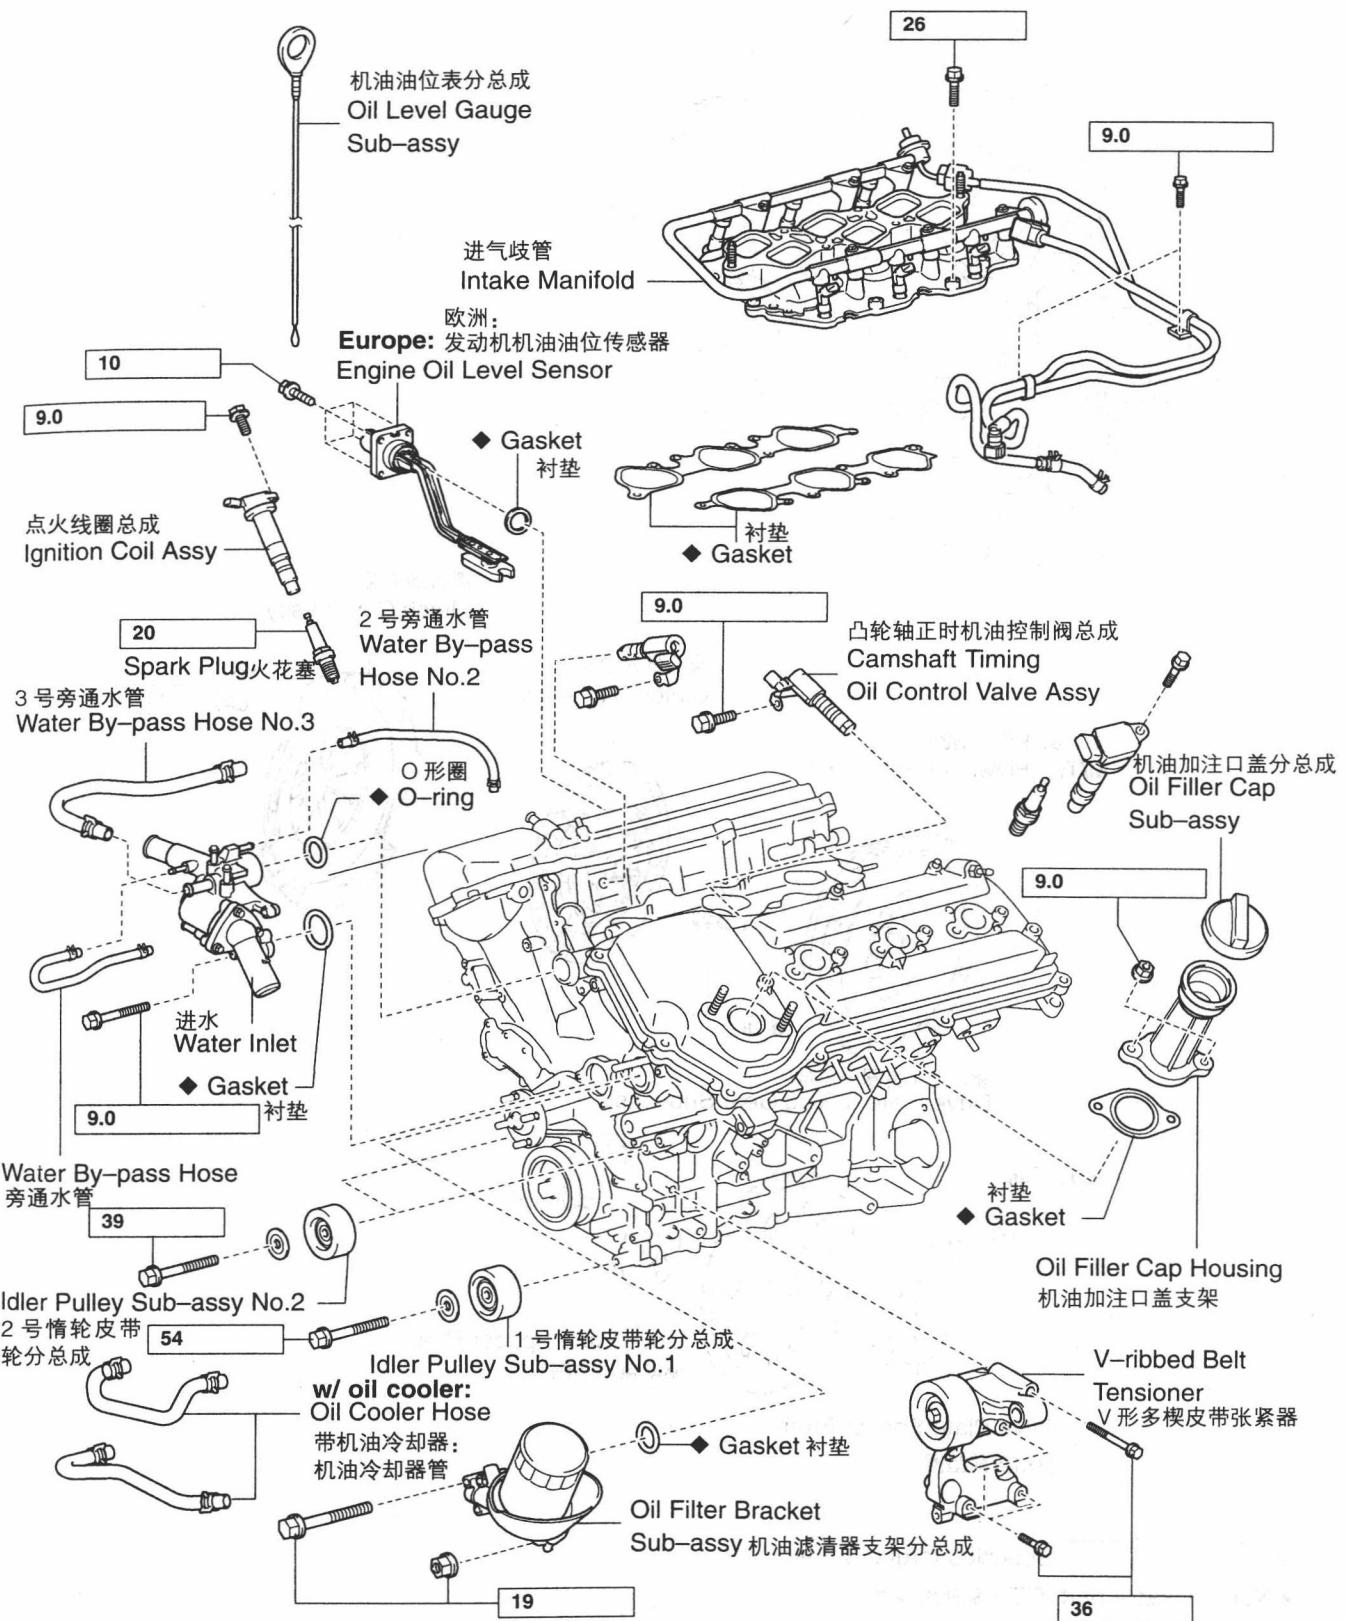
发动机总成 (ENGINE ASSEMBLY) (4)
